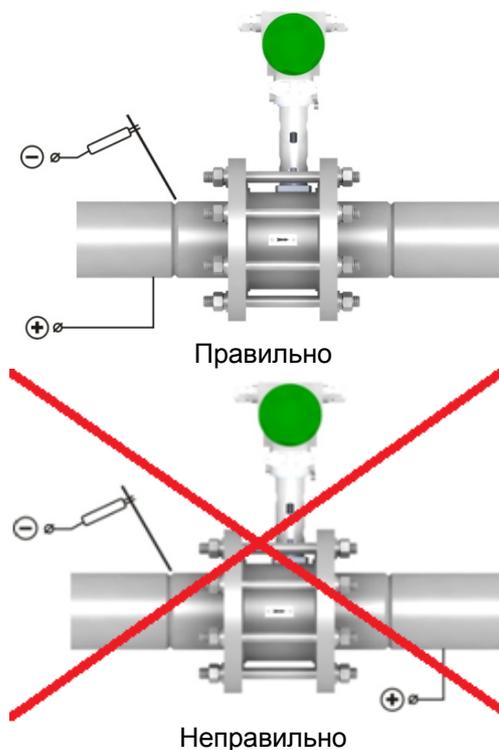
Подключение источника тока при электродуговой сварке
